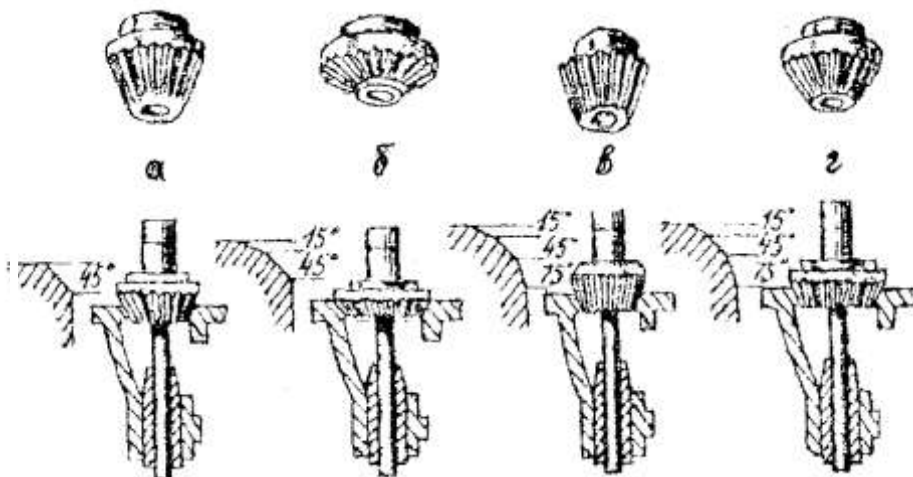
Обработка клапанноу гнезда фрезами. Фрезерование под углом: а - 45°, б - 15°, в - 75°, г - чистое фрезерование под углом 45°.
